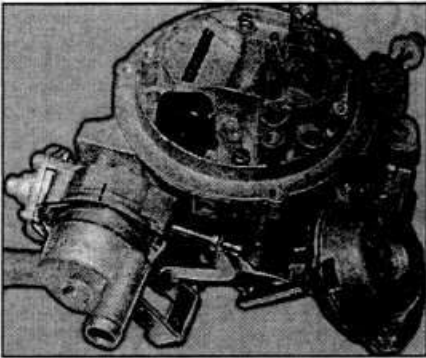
Метки на корпусах пускового устройства и биметаллической пружины для установки пружины
